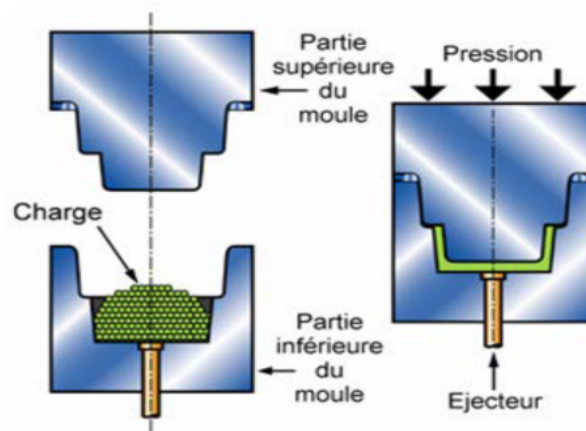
Principe de moulage par compression à froid de résine.
